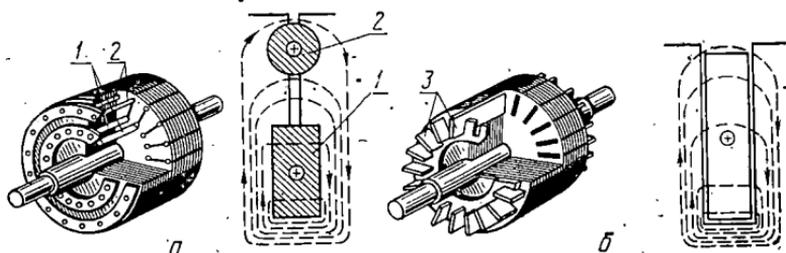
Устройство ротора с двойной клеткой и глубоким пазом:
